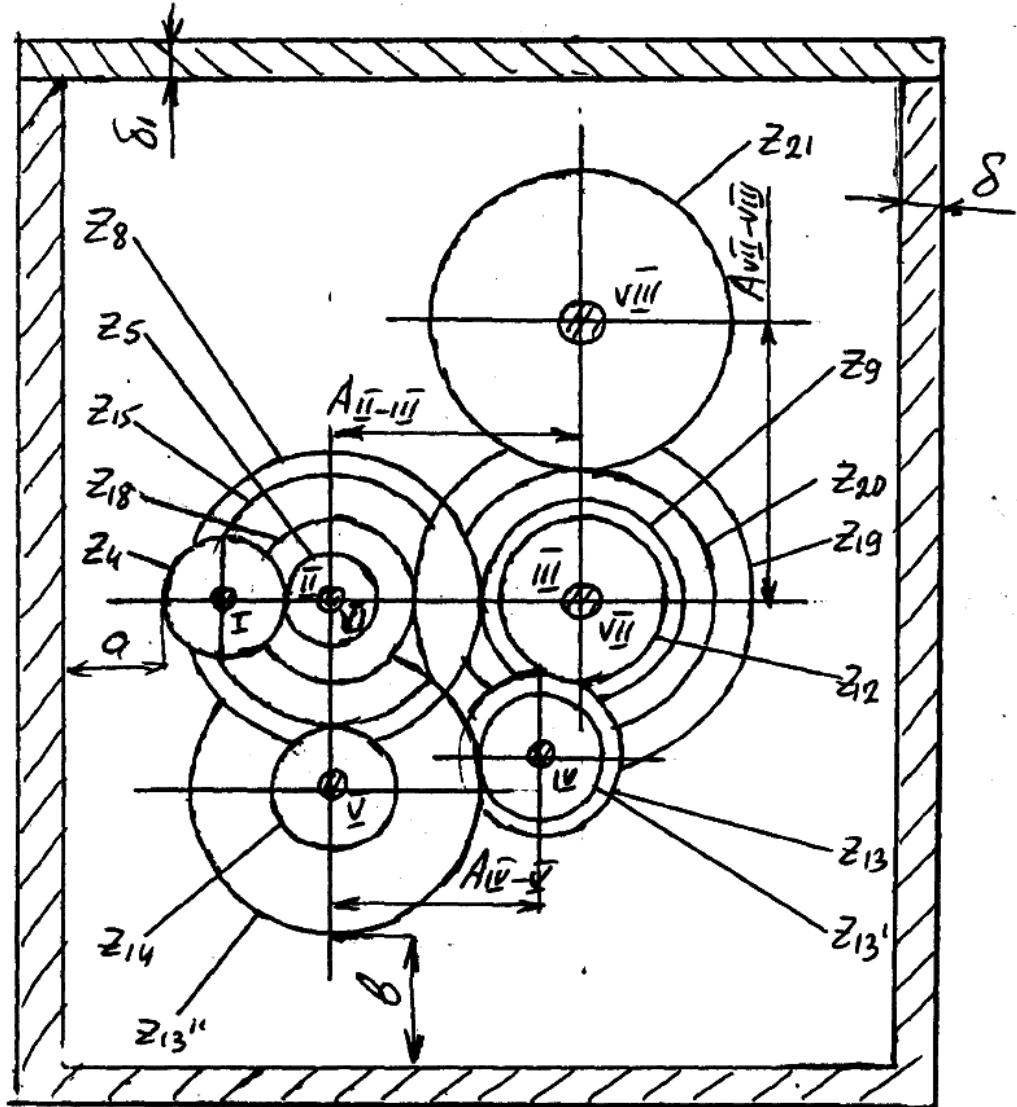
Эскизная компоновка шестерни коробки скоростей.
